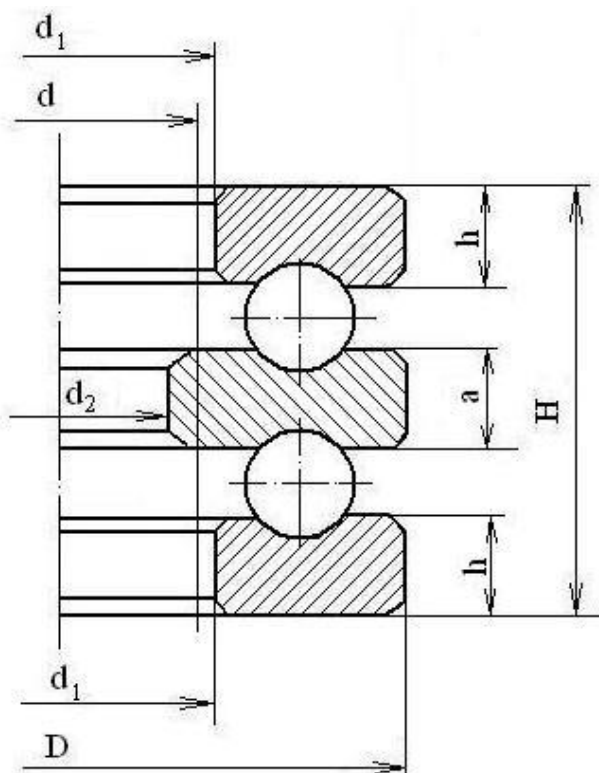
В.11 – Подшипник шариковый упорный двухрядный
